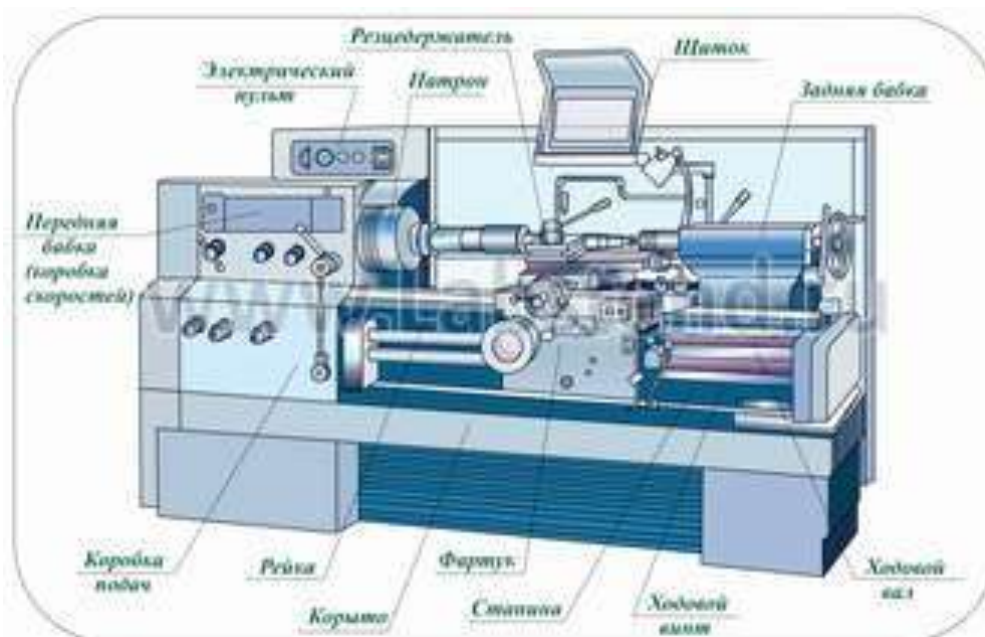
Общий вид токарно-винторезного станка 16К20
